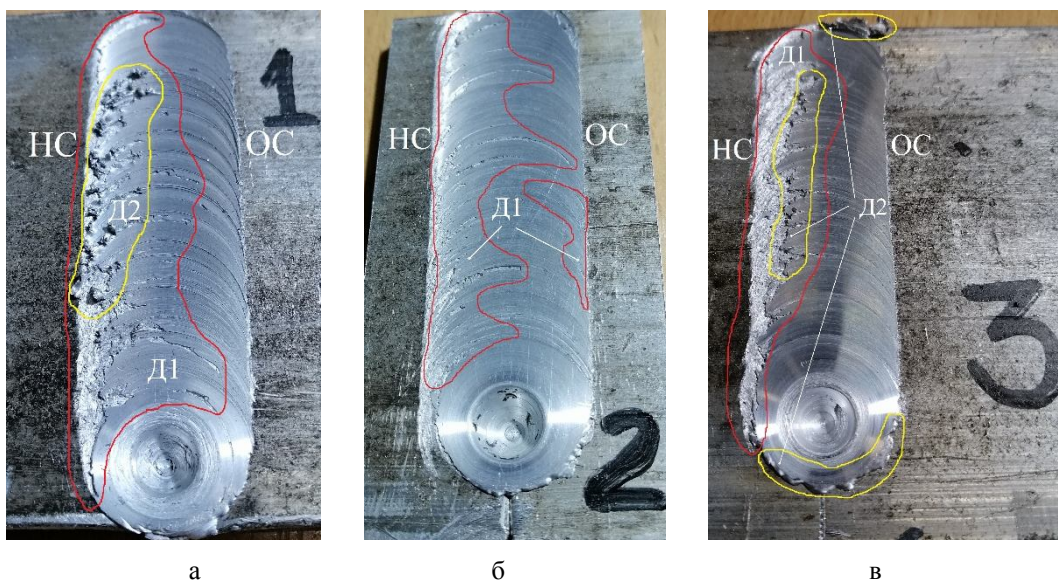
Общий вид полученных сварных соединений
